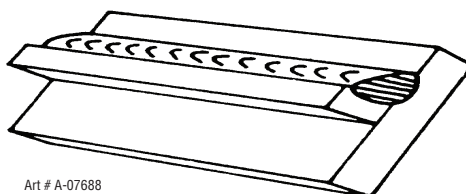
Position à plat, soudure d'angle par gravité
